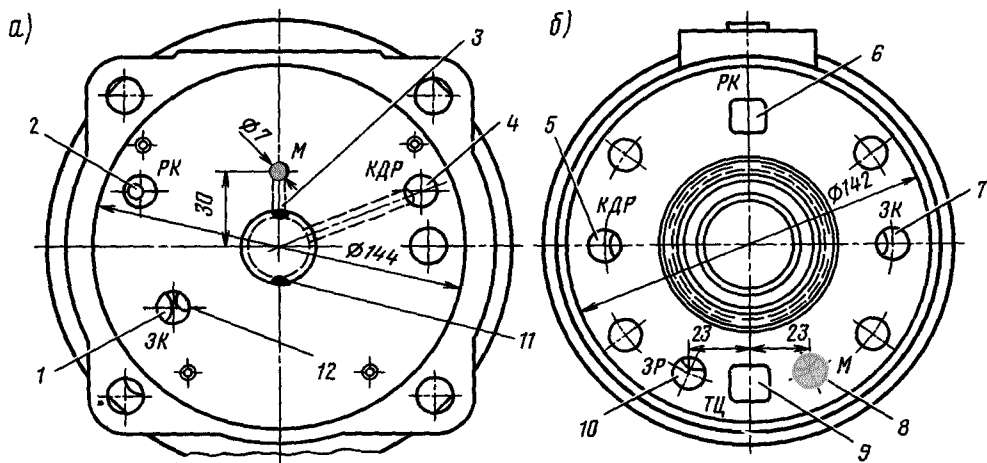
Привалочные фланцы воздухораспределителей № 270-002, 270-005-1 и 483-000.
